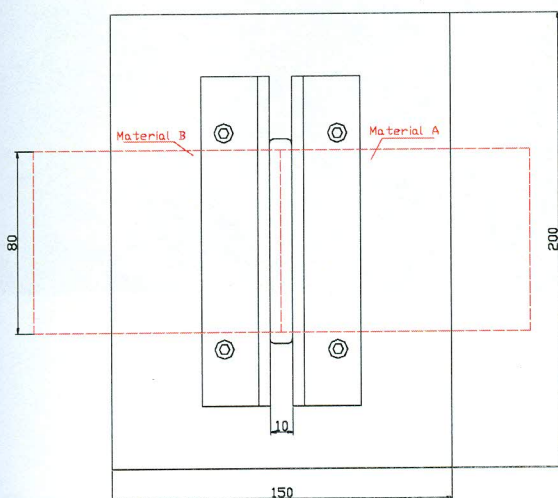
Dispositivo de posicionamento e fixação para o experimento de solda laser dos corpos de prova de tração (dimensões em mm).
